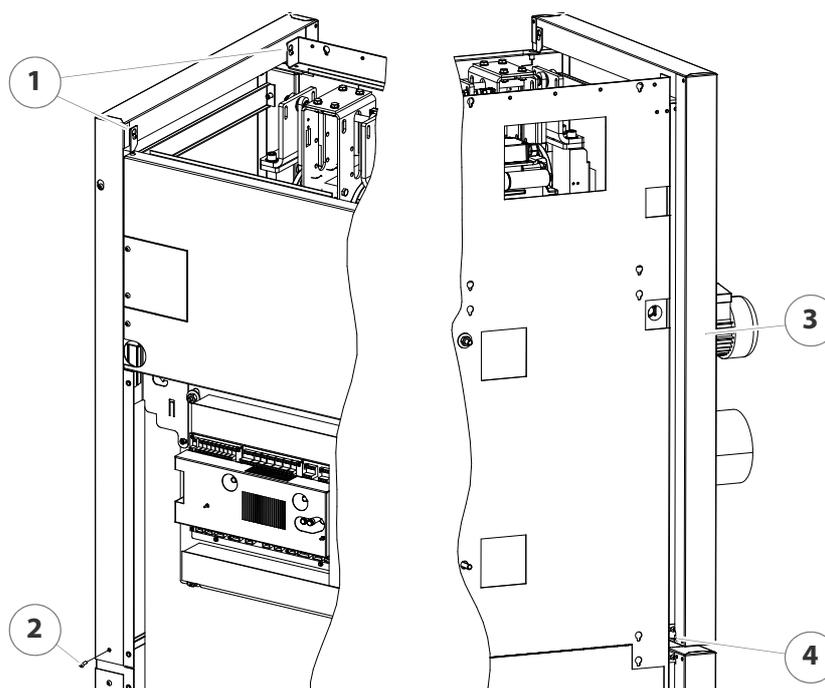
/20 - Montage des jaquettes latéral côté conduit de fumée, en haut
